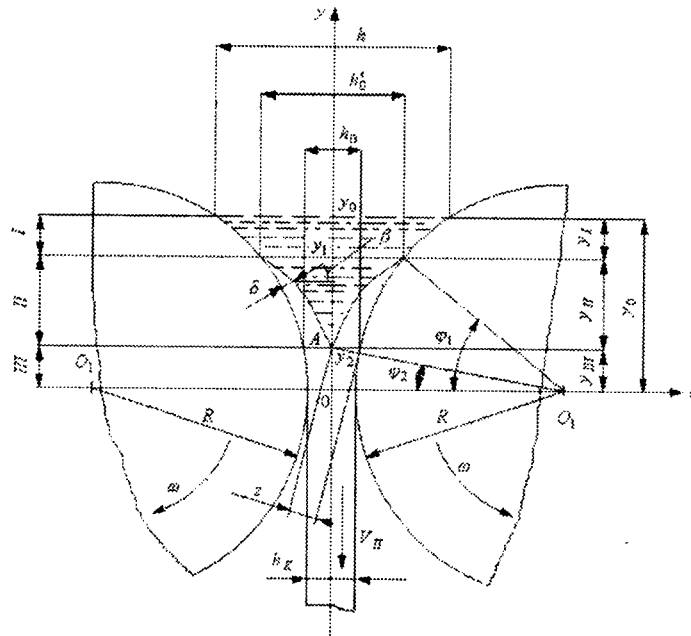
Схема процесса двухвалковой быстрой закалки расплава
